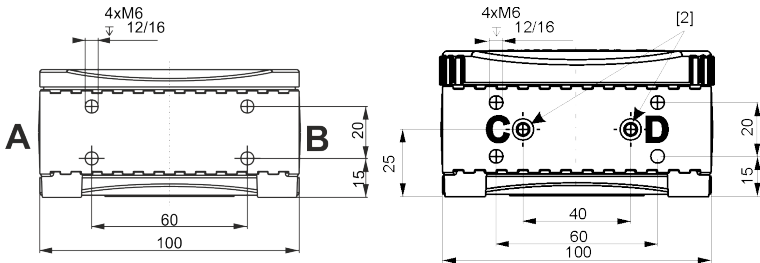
Dimensioni schema foratura (tutte le misure in mm)
